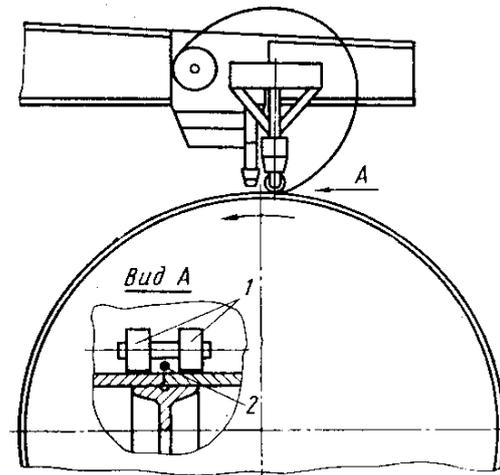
Приспособление для сборки и сварки прямолинейных стыков тонколистовых элементов
